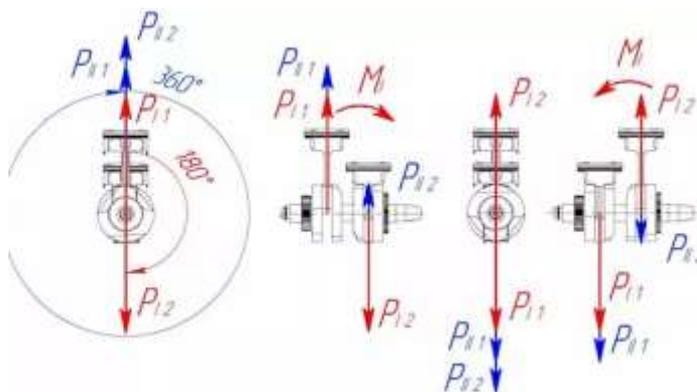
Способы балансировки двухцилиндрового двигателя
